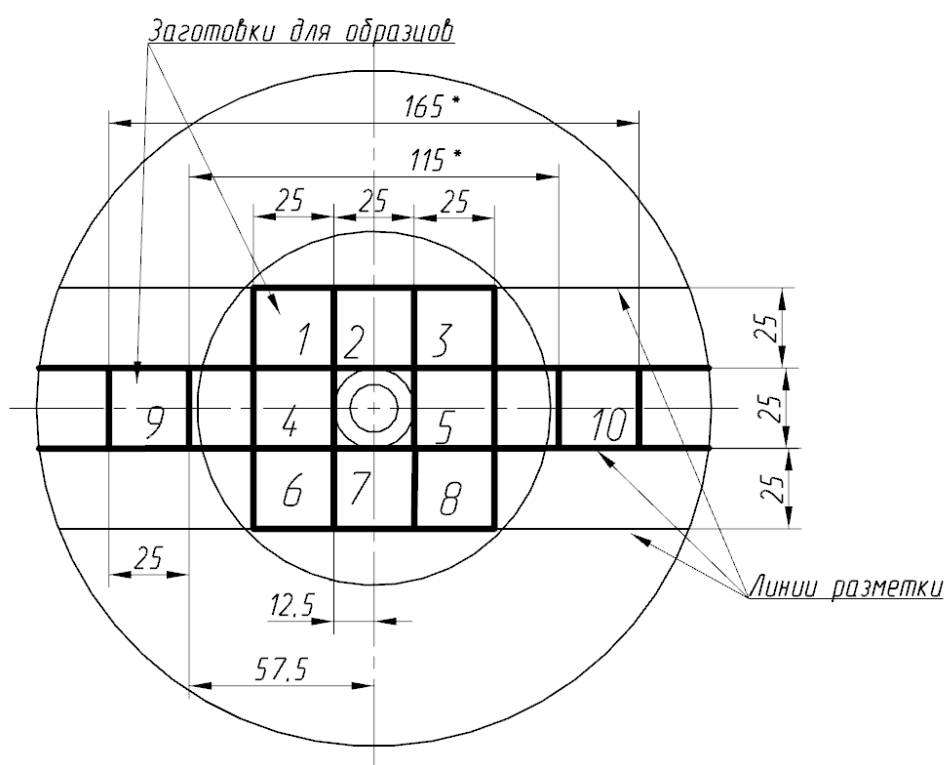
Чертеж выпилки образцов для испытаний (вид сверху)
